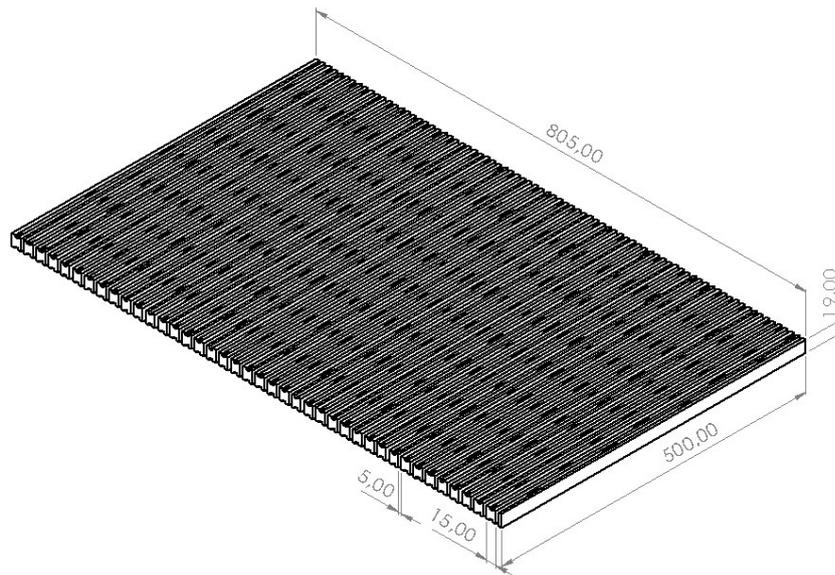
Desenho técnico da placa Janus (Medidas em mm)
